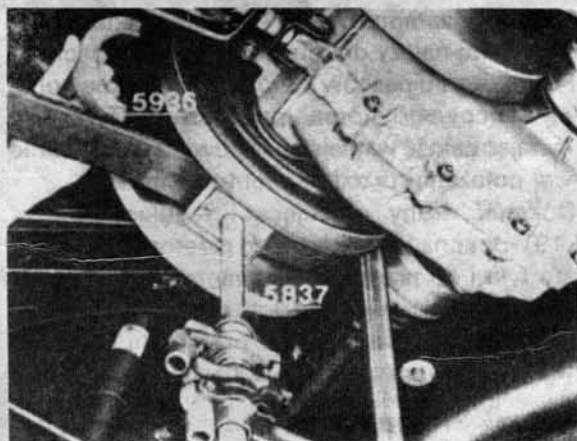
Блокировка шкивов ременной передачи при снятии клиновых ремней коробки CVT
